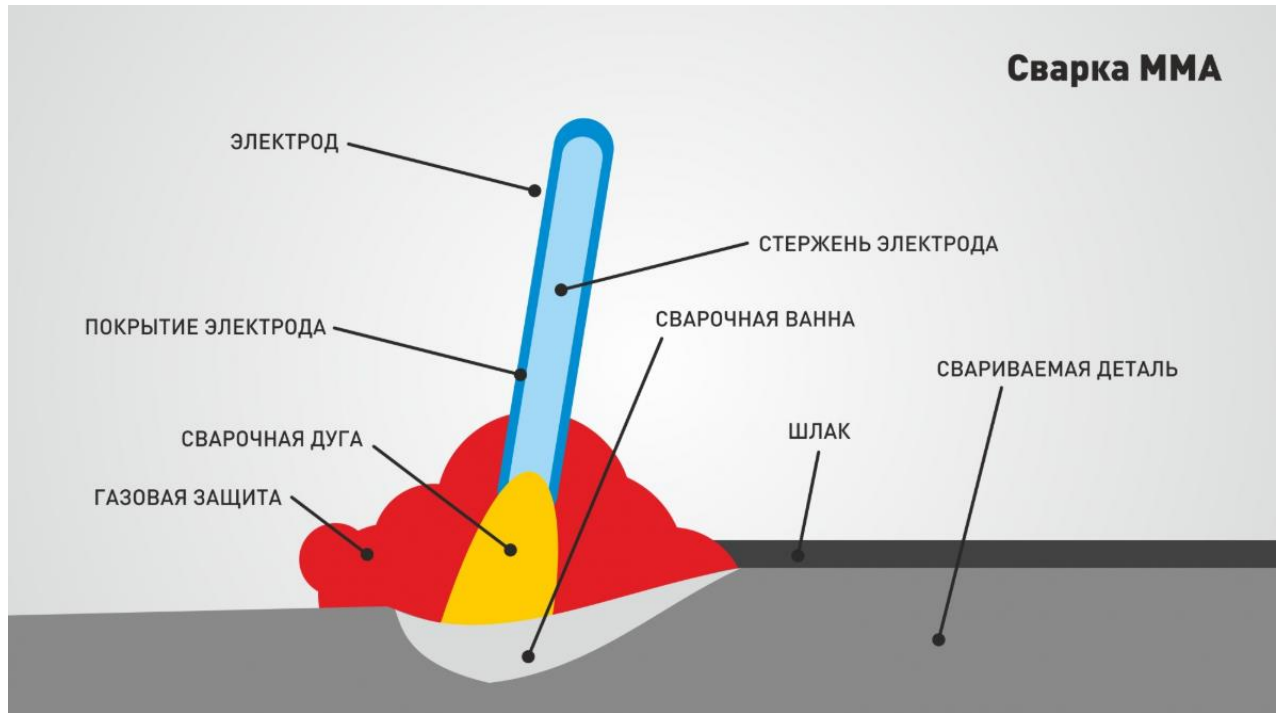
ММА зварювання. Ресурс [39]
